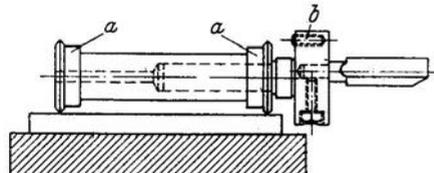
Auswuchtgerät für Futter mit exzentrischem Bohrer an Oberfräsen. a = Auswuchtrollen; b = Auswuchtschraube.
